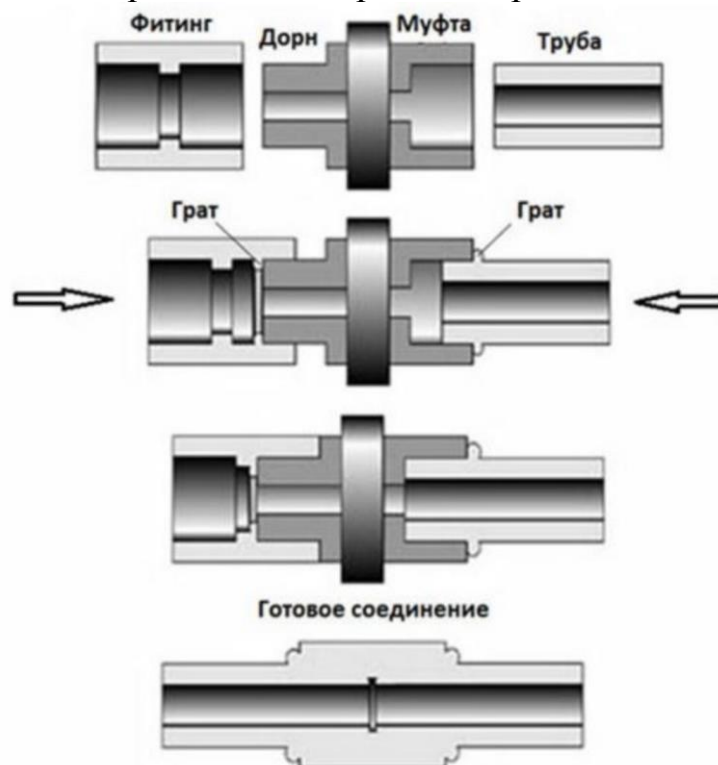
Раструбная сварка пластмассовых труб
